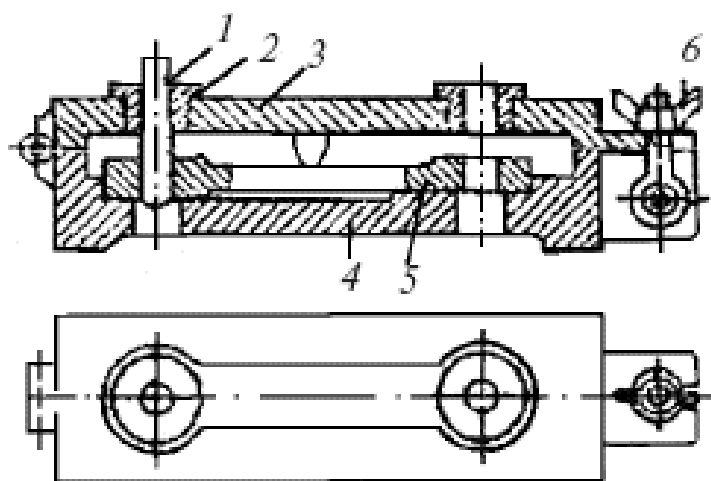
Приспособление с кондукторной плитой для сверления: 1 – сверло; 2 – втулка; 3 – кондукторная плита; 4 – нижняя часть кондуктора; 5 – обрабатываемая деталь; 6 – винт с гайкой-барашком
